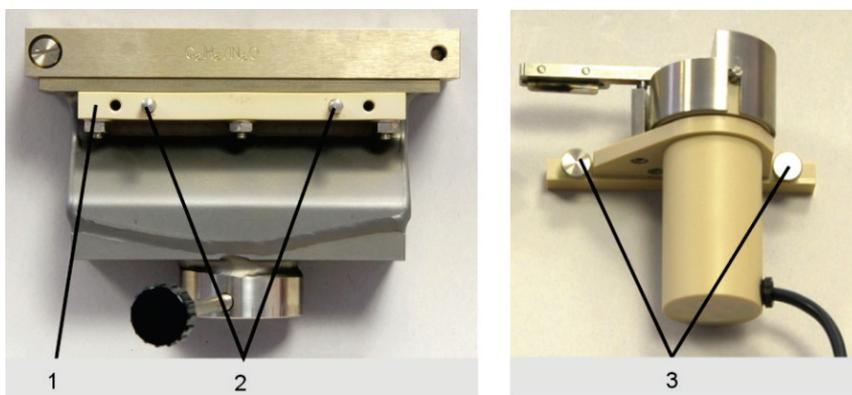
Riel de montaje / tornillos moleteados en el raspador
